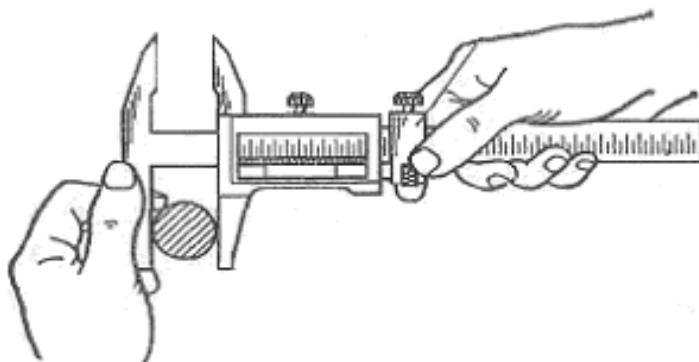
Измерение наружного размера детали штангенциркулем
